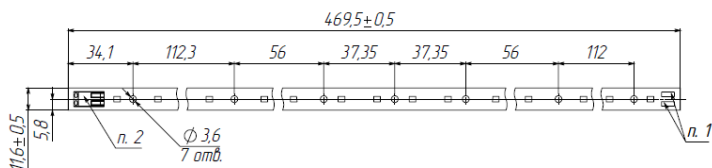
Внешний вид с габаритными и присоединительными размерами СДПП TRN-Line-11W-20-2835-1002 серии FLASH
